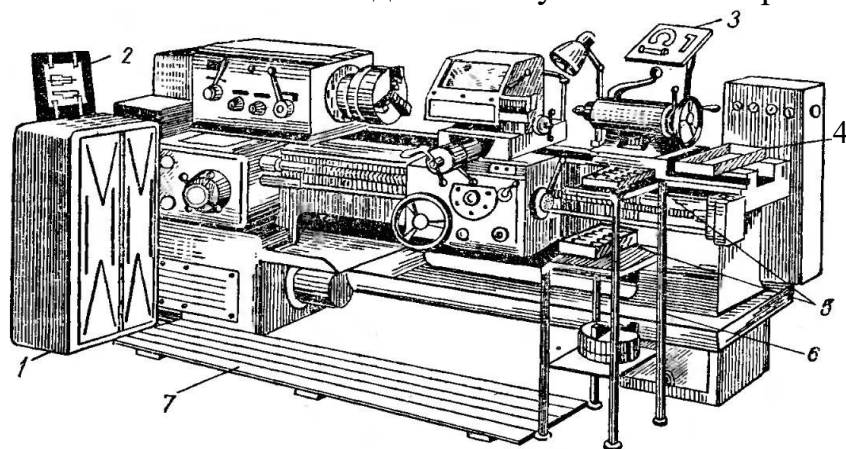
Планування робочого місця токаря: 1 – інструментальна тумба; 2 – планшетка з кресленням деталі; 3 – планшетка для контрольовимірювальних інструментів; 4 – лоток для ключів; 5 – ящики із заготовками; 6 – підставка; 7 – дерев'яна решітка
